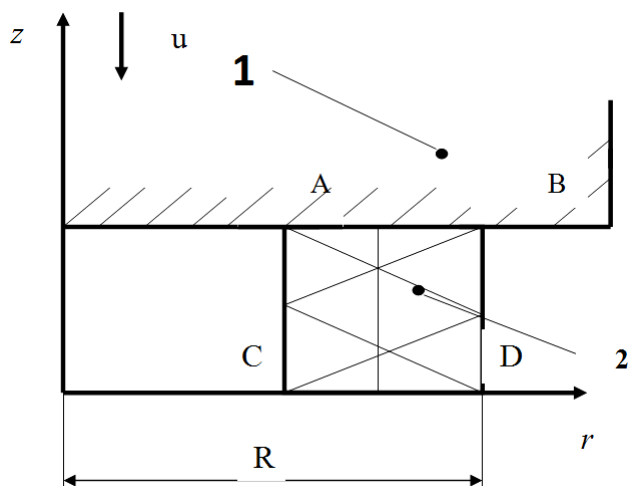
Розрахункова схема процесу опаді асиметричної заготовки: 1 - плита, 2 - заготовка, u - напрямок переміщення, R - радіус заготовки
